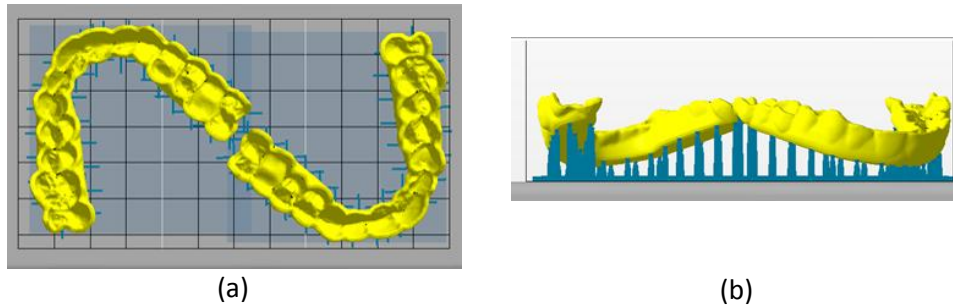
a) Vista en planta de las férulas colocadas en la plataforma de impresión. b) Vista lateral de las férulas colocadas en la plataforma a 20º respecto de la horizontal.
